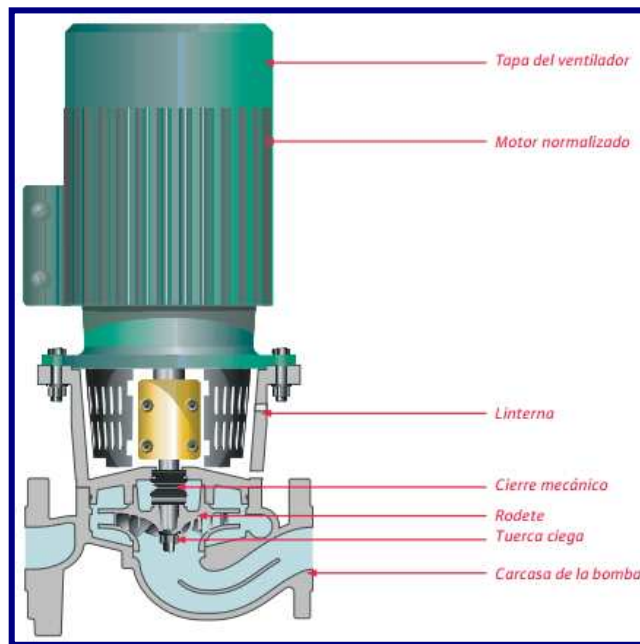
Principales partes de una bomba de rotor seco (www.wilo.es)
